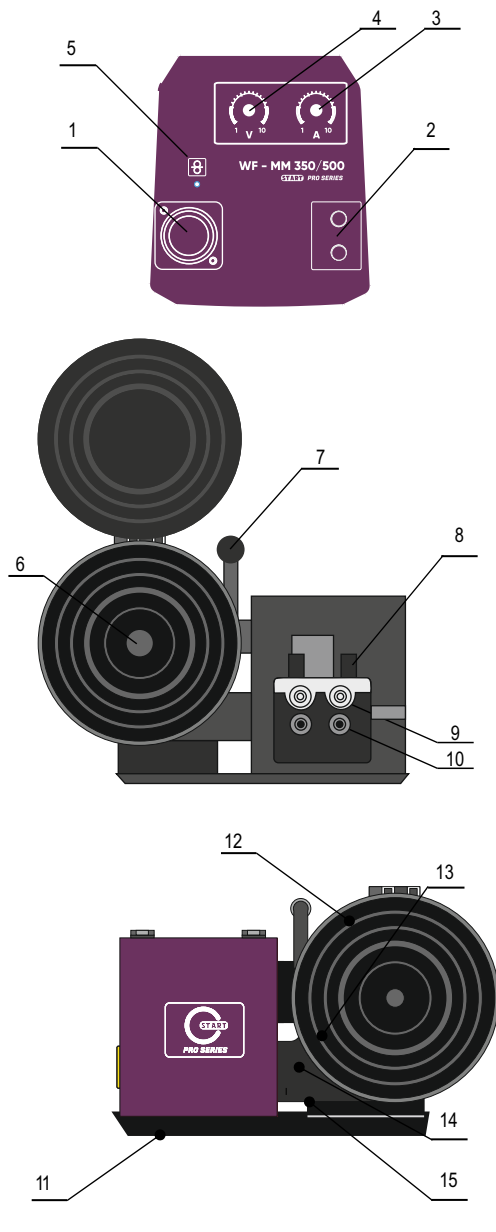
Устройство подачи сварочной проволоки
